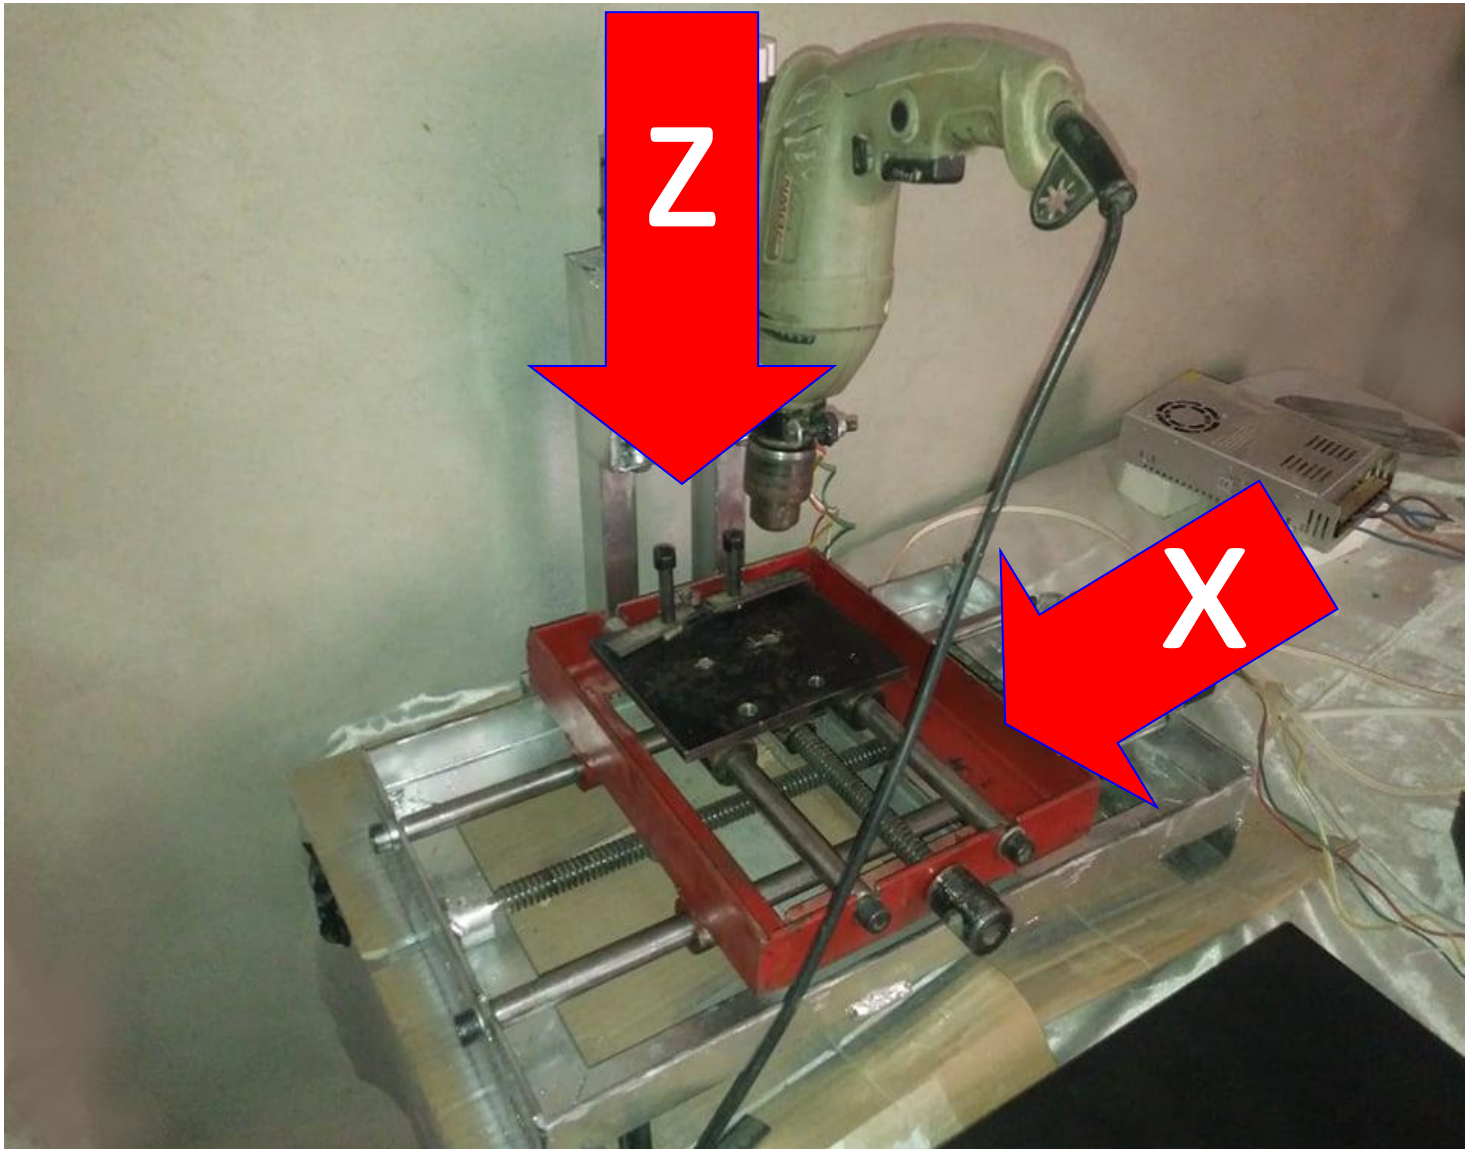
La forme finale de la machine de soudage par friction malaxage.
